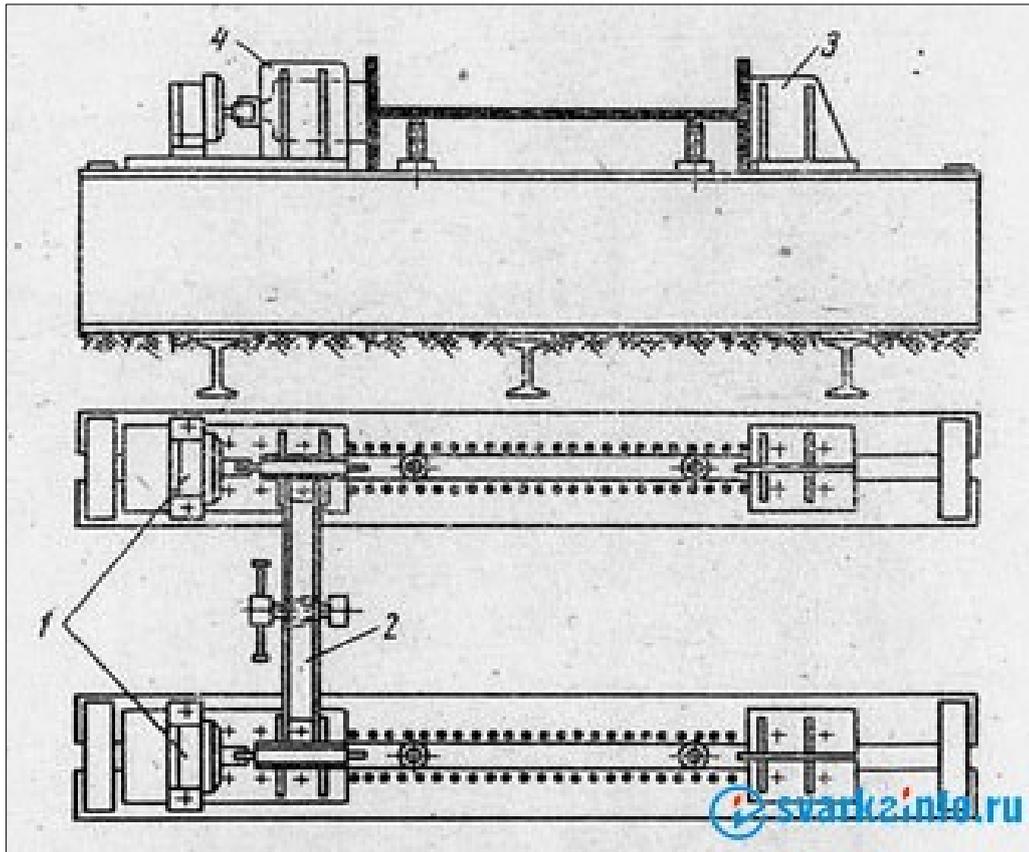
Устройство сборочного кондуктора с пневматическими прижимами: 1 — пневматические цилиндры; 2 — переносная траверса; 3 — неподвижный упор; 4 — направляющие подвижного упора.
